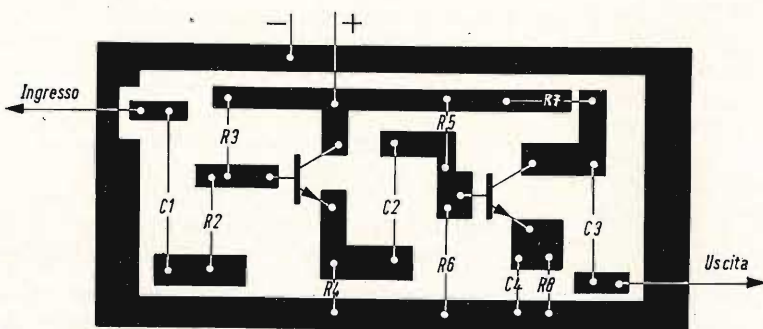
Circuito stampato adatto per il montaggio di fig. 1.
